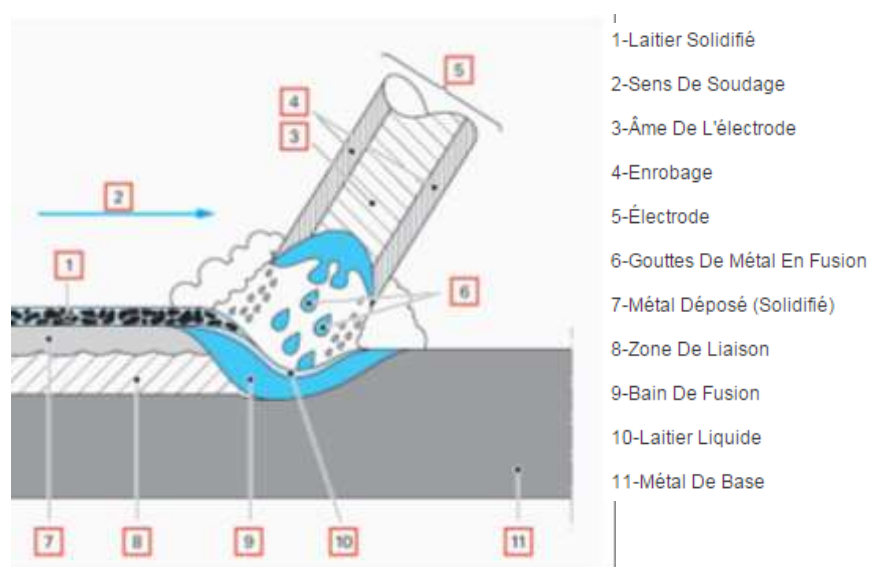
Principe du procédé de soudage SMAW.
